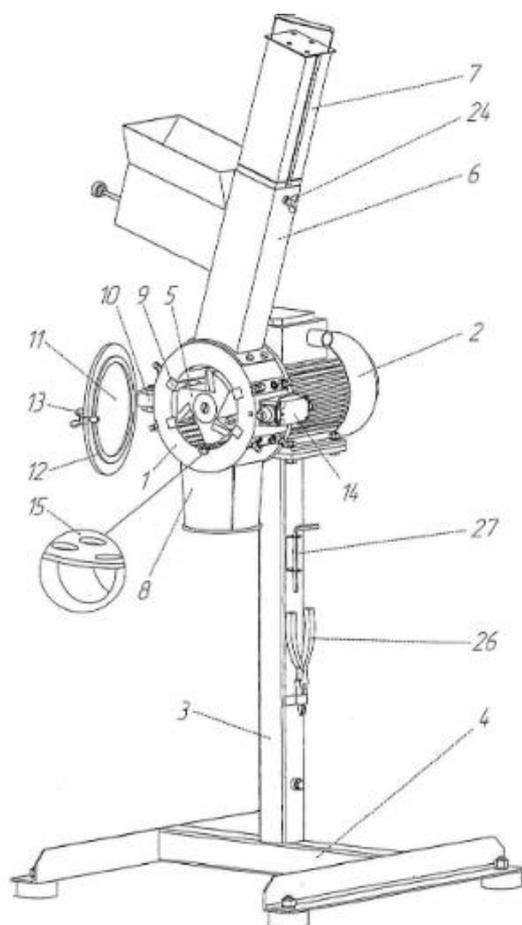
Общий вид роторной ножевой мельницы РМ 120
